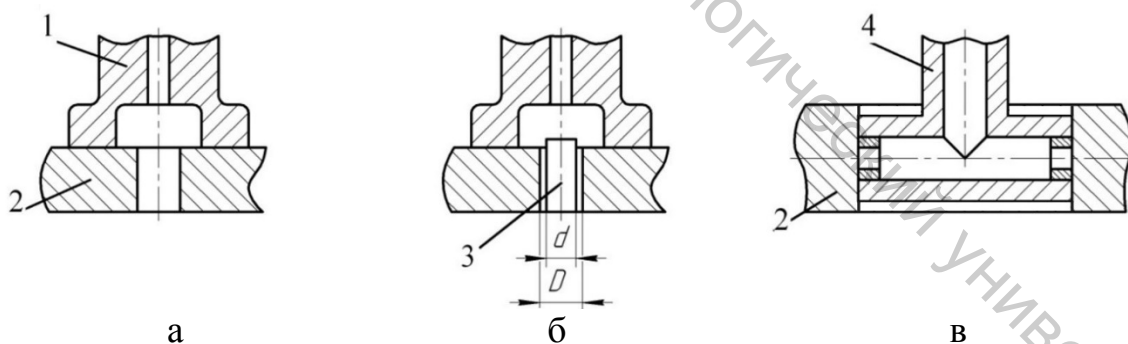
Схемы измерений отверстий пневматическим способом:
